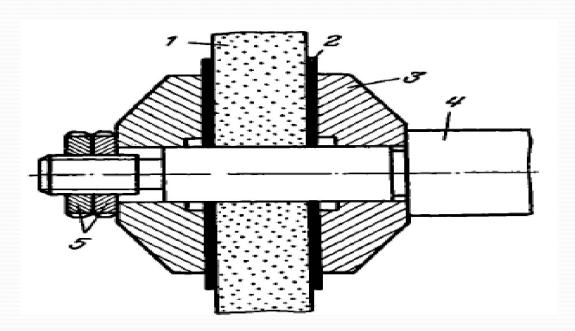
Схема крепления заточного круга на шпинделе заточного станка 1 – круг; 2 – прокладка; 3 – фланец; 4 - шпиндель; 5 – тайка.
